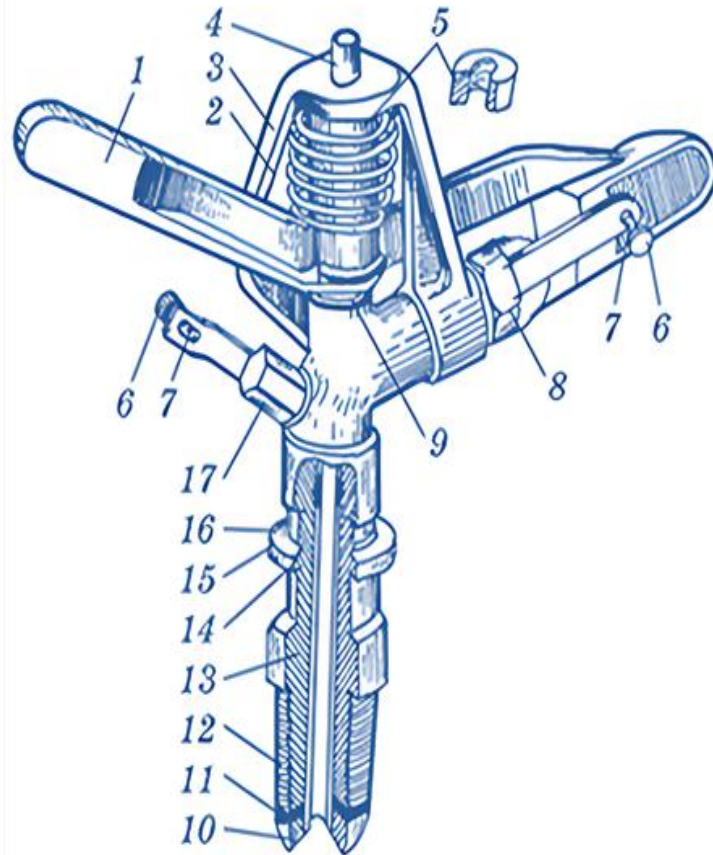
Далекоструминний дощувальний апарат з реактивною лопаткою: 1 – реактивна лопатка; 2 – корпус; 3 – пружина кручення; 4 – вертикальна вісь; 5 – гайка; 6 – гвинт-розсікач; 7 і 16 – пружини; 8 і 17 – насадки; 9 і 11 – шайби; 10 – патрубок; 12 – різьба; 13 – головка під ключ; 14 – ущільнення; 15 – патрубок
